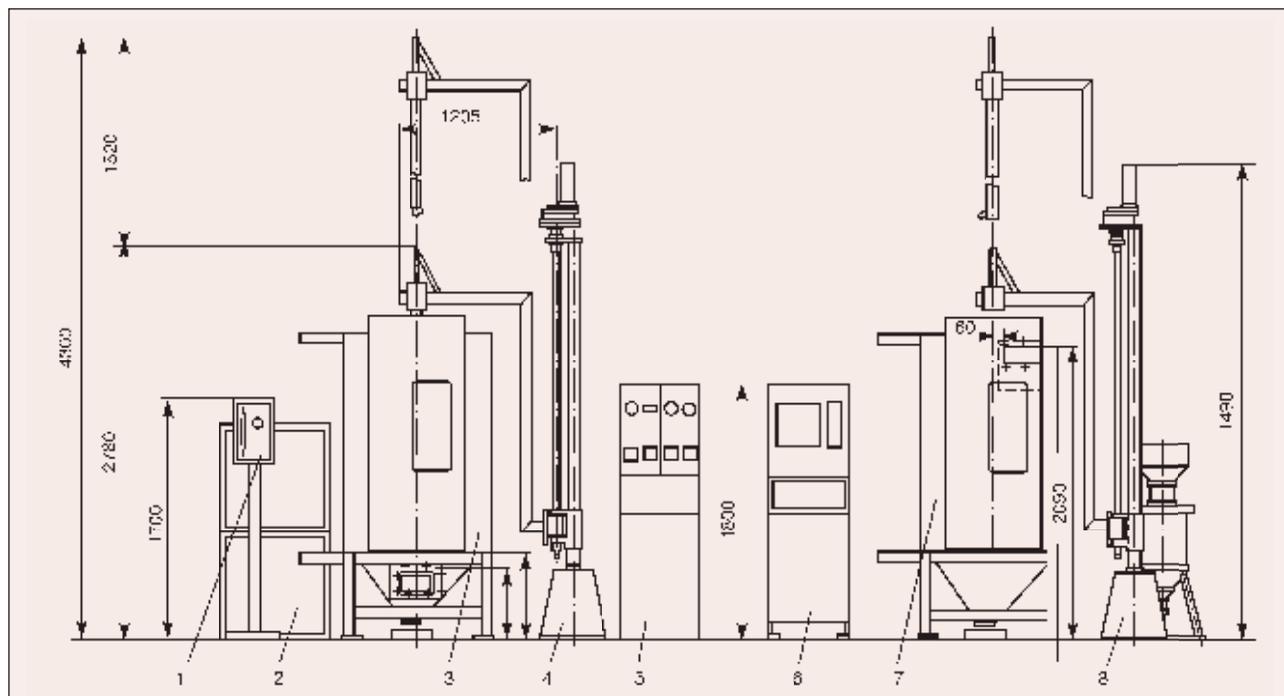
Схема линии плазменного напыления покрытий PLAZER ISS-75-PL на рабочие поверхности гильз судовых и локомотивных двигателей
